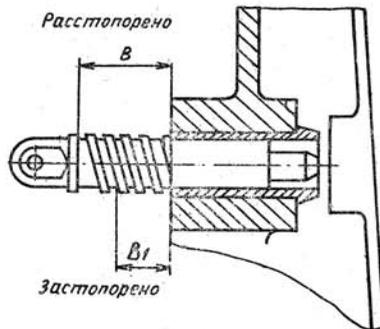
Измерение величины захода стопора в гнездо и зазора между горцевой поверхностью стопорного пальца и наружной поверхностью стопорного гнезда
